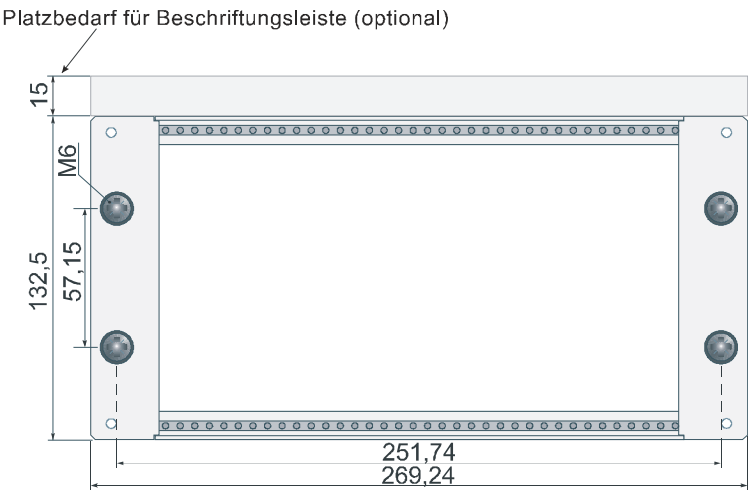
Vorderansicht des Baugruppenträgers Type BGT05 mit Beschriftungsleiste
